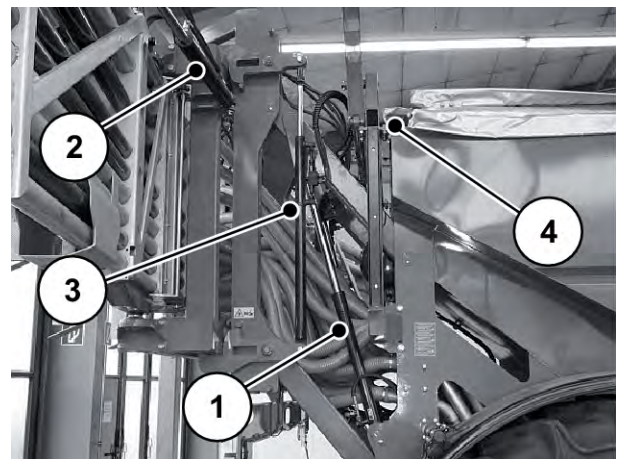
Hydraulikzylinder Ausleger hinten rechts
